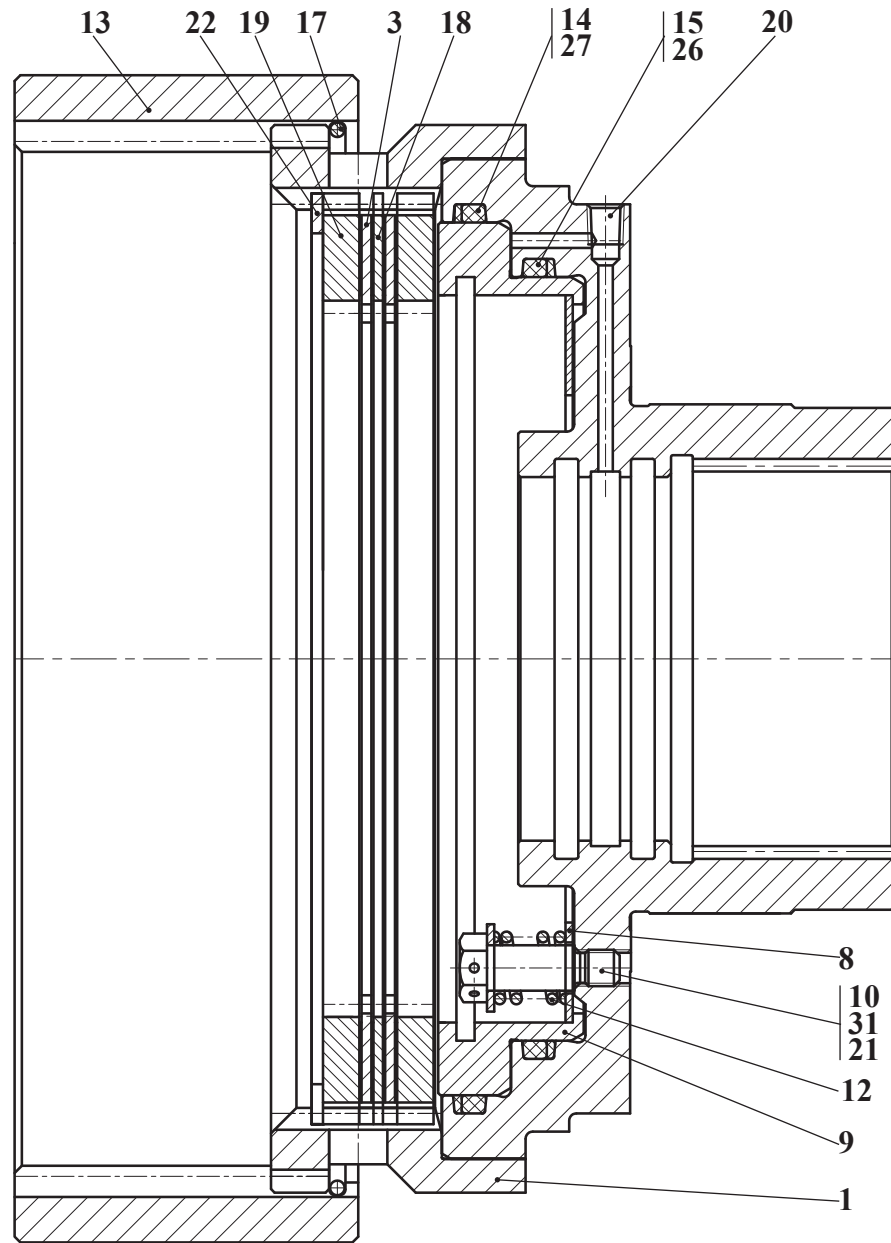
У2210.20Н-2-03.100-03-Б	Тормоз колесный
